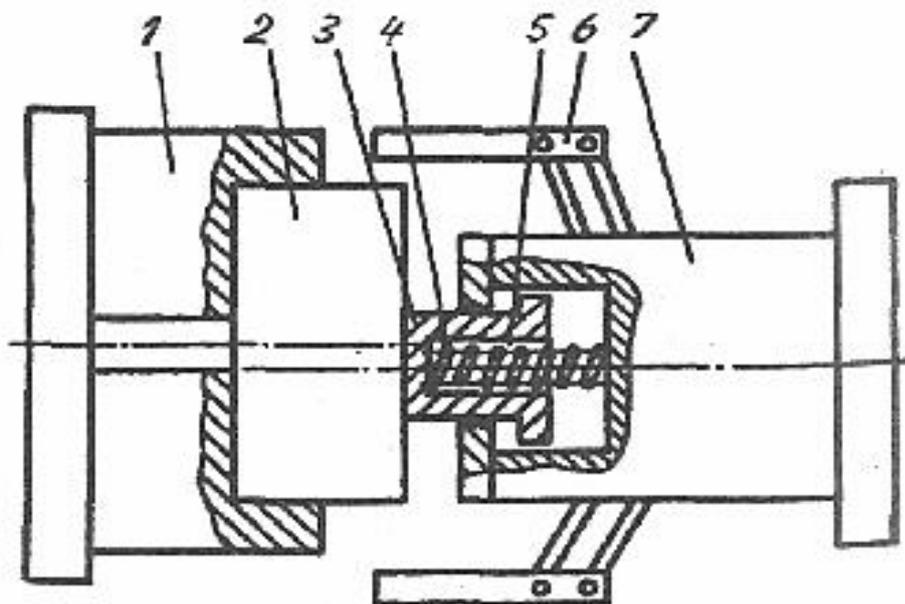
Захватное устройство для установки заготовки в патрон
